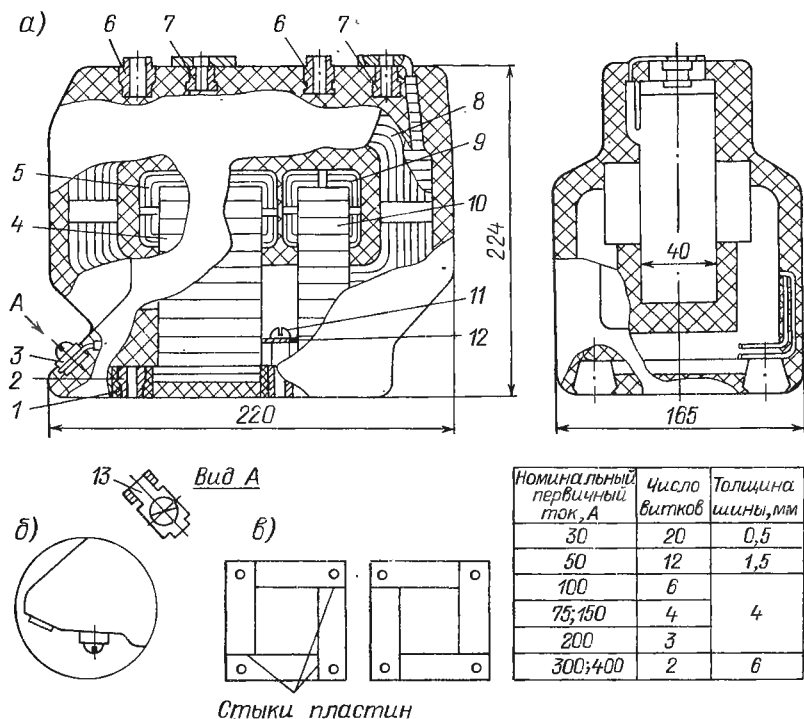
Трансформатор тока ТЛК10 на номинальные токи до 400 А: а — конструктивные варианты 1 и 3; б — конструктивные варианты 2 и 4; в — схема шихтовки магнитопровода измерительной обмотки
